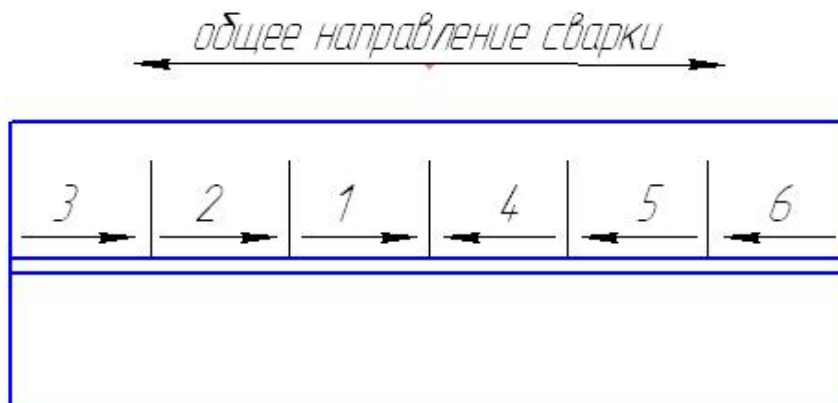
Схема сварки обратноступенчатым способом от середины к краям
